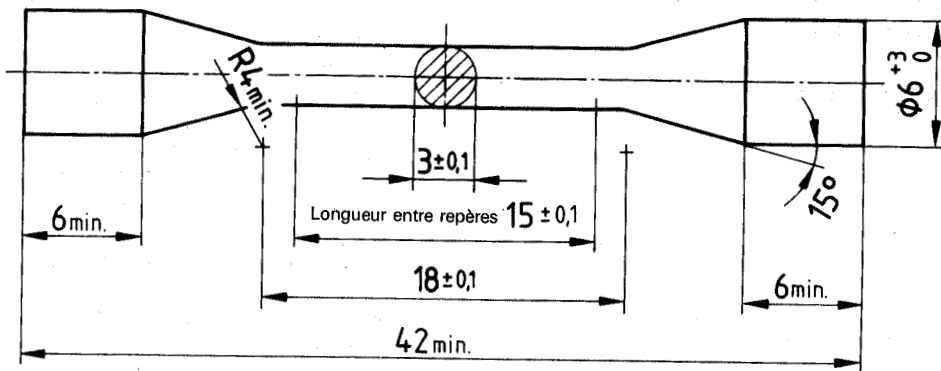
Éprouvette à extrémités cylindriques<sup>1)</sup>
